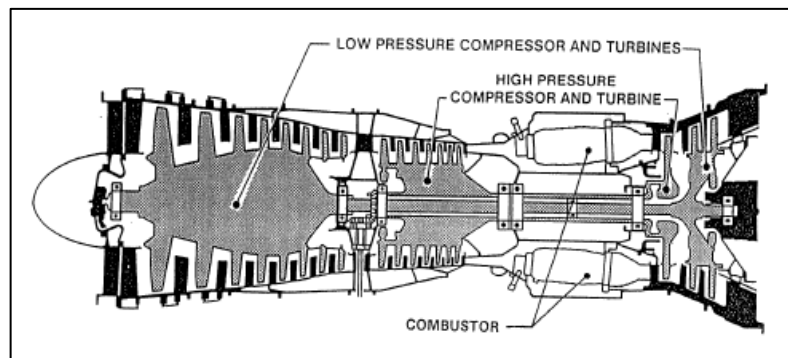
Esquema partes Turbina Pratt & Whitney.
